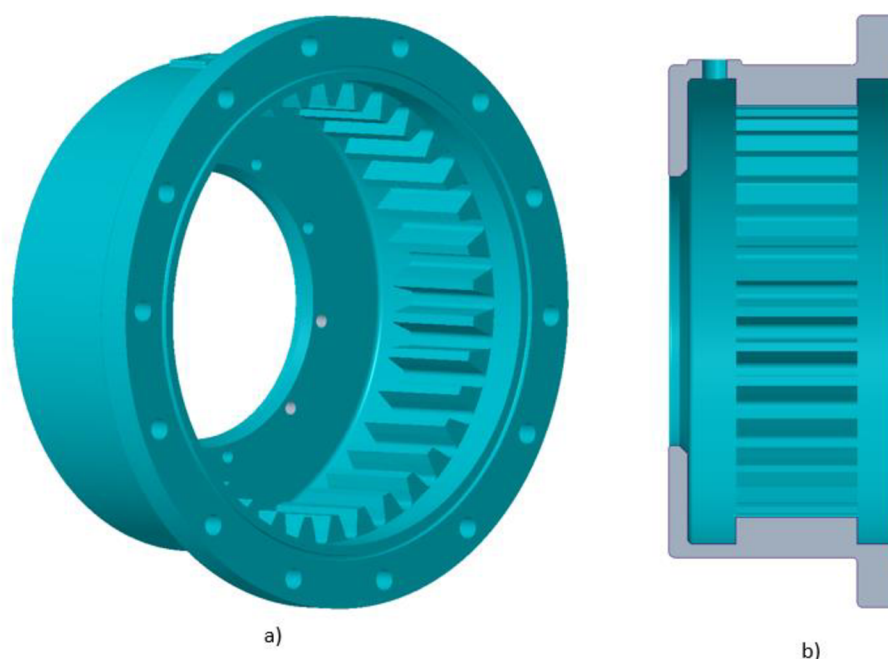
Náboj spojky a) v obecném pohledu b) v řezu
